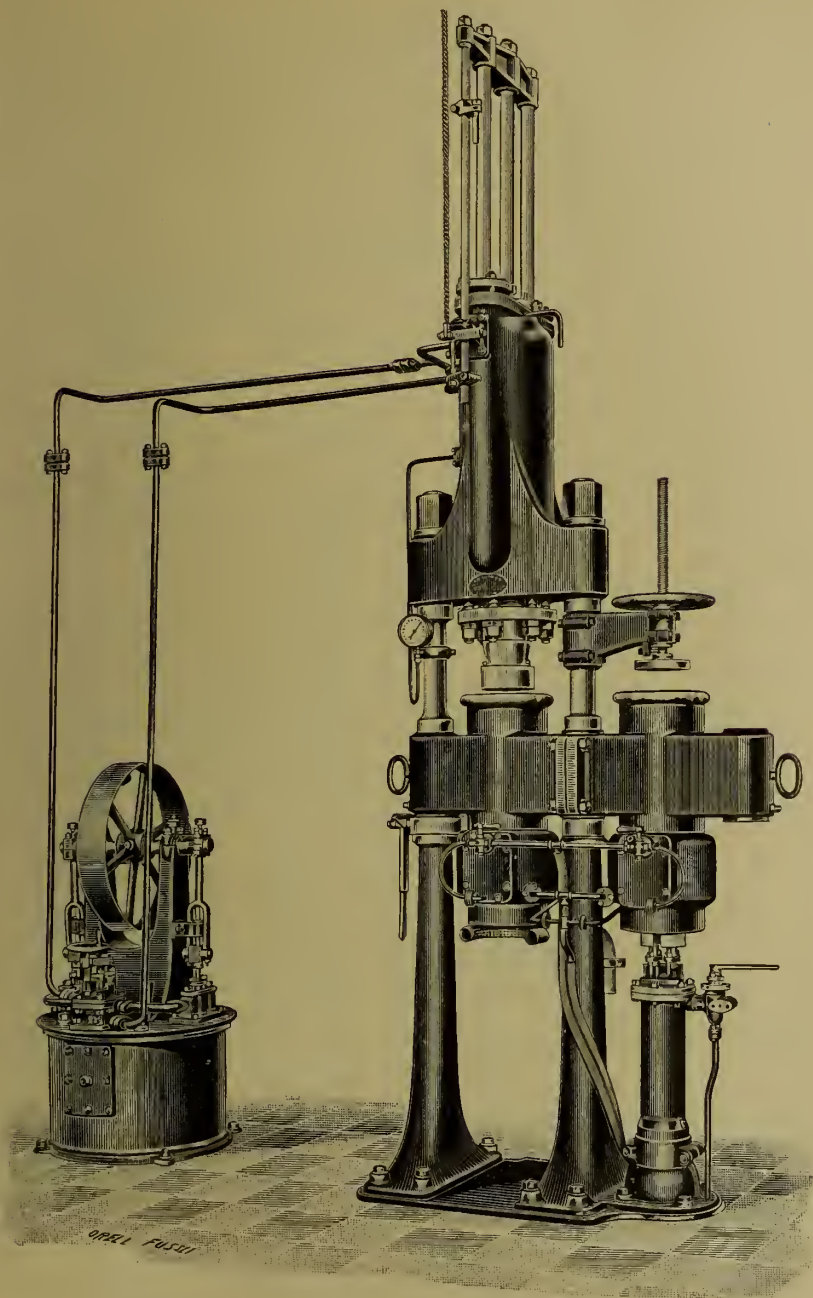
Stehende hydraulische Presse der Maschinenfabrik
